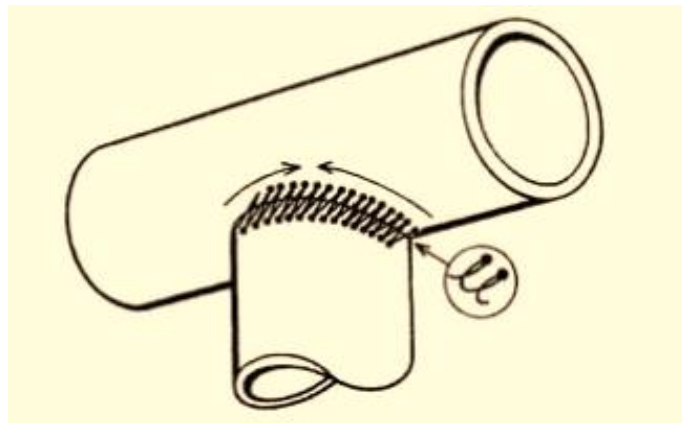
Modèle de tissage pour le soudage de raccord en T avec un tuyau croisé sous le pipe horizontal. [45]
